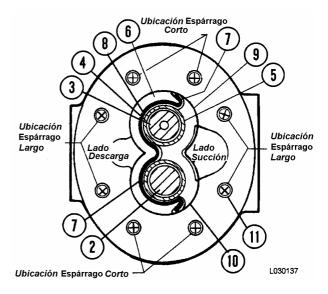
REENSAMBLADO DE LA BOMBA
